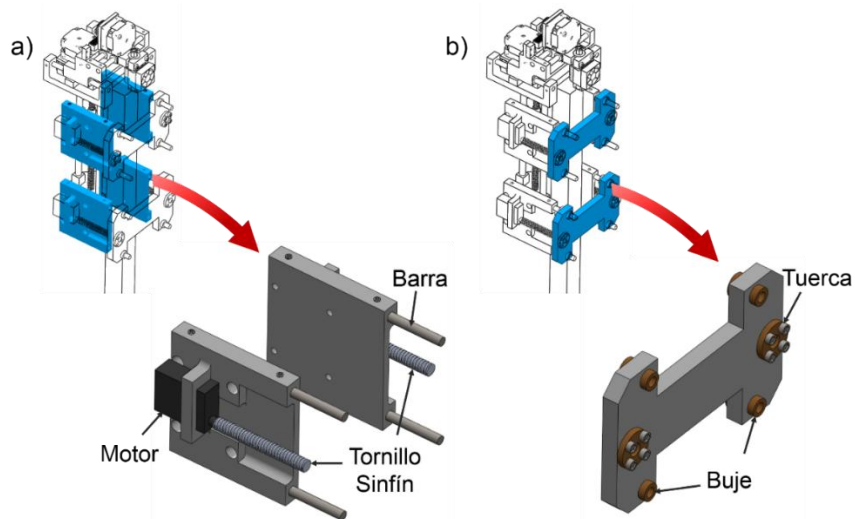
Piezas del diseño preliminar que componen ambos mecanismos de sujeción. En (a) se muestra la base del sistema motriz la cual permite el acoplamiento del motor acoplado al tornillo sinfín y las barras que guían el movimiento de la (b) mordaza móvil.
